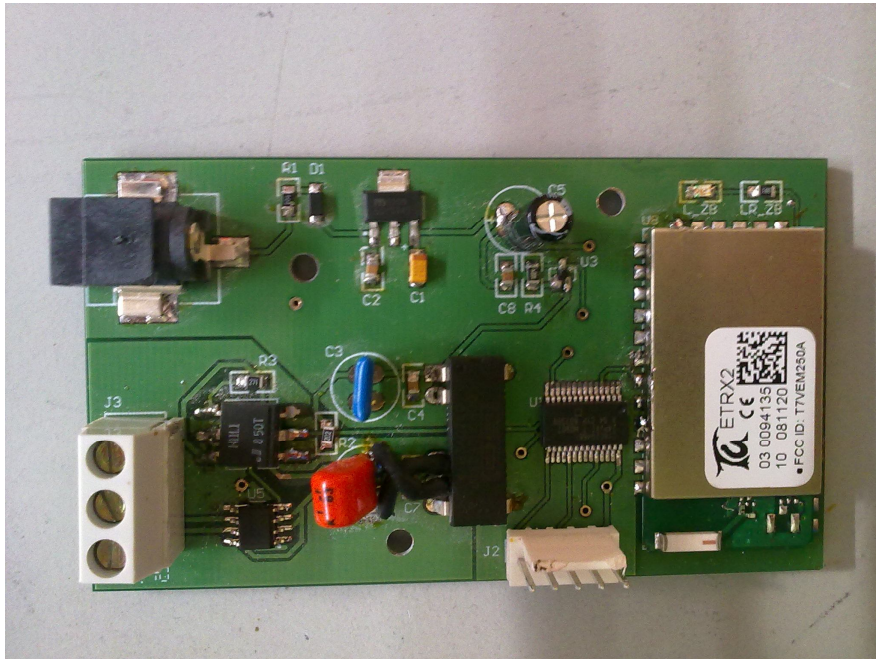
Imagen de la cara superior del montaje final de la PCB
